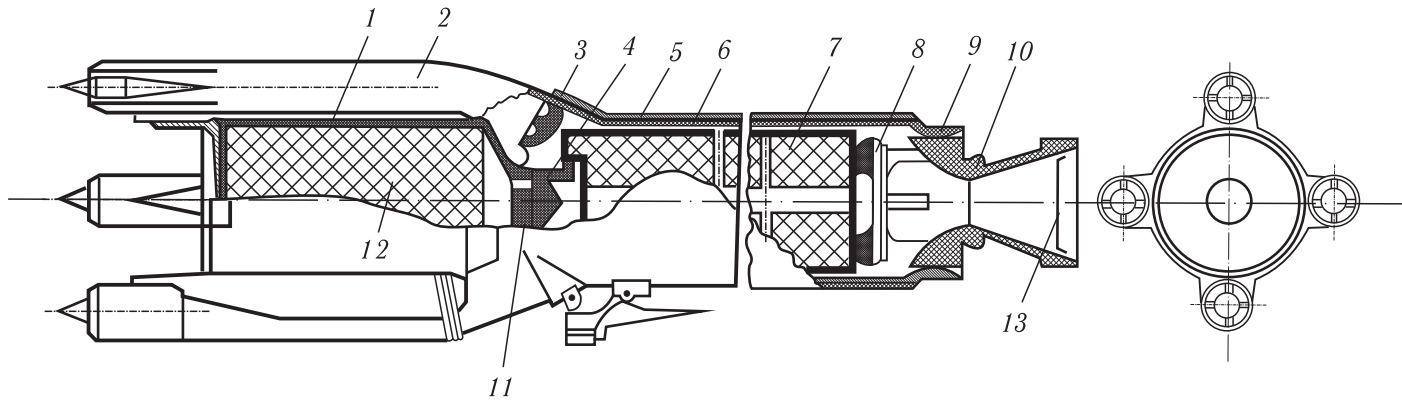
Схема ИРПДТ ракеты AKASH: 1 — корпус газогенератора, 2 — патрубок ВЗУ, 3 — заглушка выходного отверстия ВЗУ, 4 — передняя опора заряда стартового ТРТ, 5 — корпус камеры сгорания, 6 — теплозащитное покрытие, 7 — вкладной заряд ТРТ, 8 — задняя опорная решетка заряда стартового ТРТ, 9 — маршевое сопло, 10 — стартовое сбрасываемое сопло, 11 — сопловая распределительная головка газогенератора, 12 — заряд маршевого ТРТ, 13 — мембрана для герметичности
